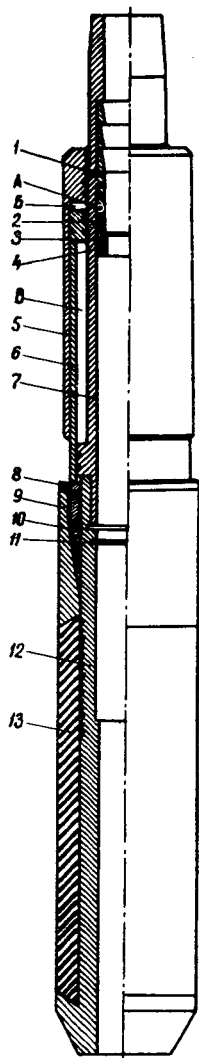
Разбуриваемый пакер ПР-1 (214) : 1,4 - штифт; 2- втулка; 3- седло; 5 - цилиндр; 6- выдвижной стакан; 7- корпус; 8-кольцо; 9-втулка; 10-плашка; 11-стопорное кольцо; 12-корпус; 13-резиновый элемент; А-отверстие; Б-гидравлическая камера; В - воздушная камера .
